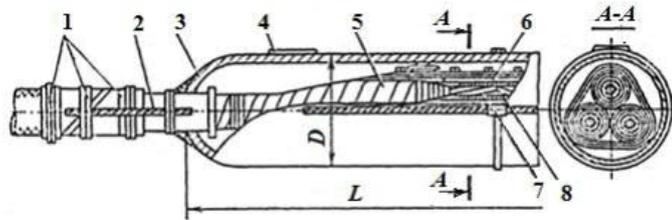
Соединительная муфта в свинцовом корпусе для кабелей на напряжение 6, 10 кВ: 1 – бандаж; 2 – заземляющий провод; 3 – корпус муфты; 4 – заливочное отверстие; 5 – изоляция кабеля; 6 – подмотка из бумажных лент; 7 – токопроводящая жила; 8 – соединительная гильза
